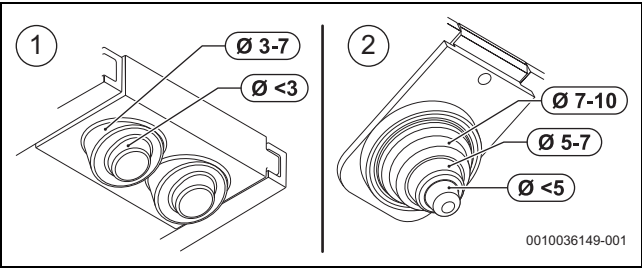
Adaptar las abrazaderas al diámetro del cable
